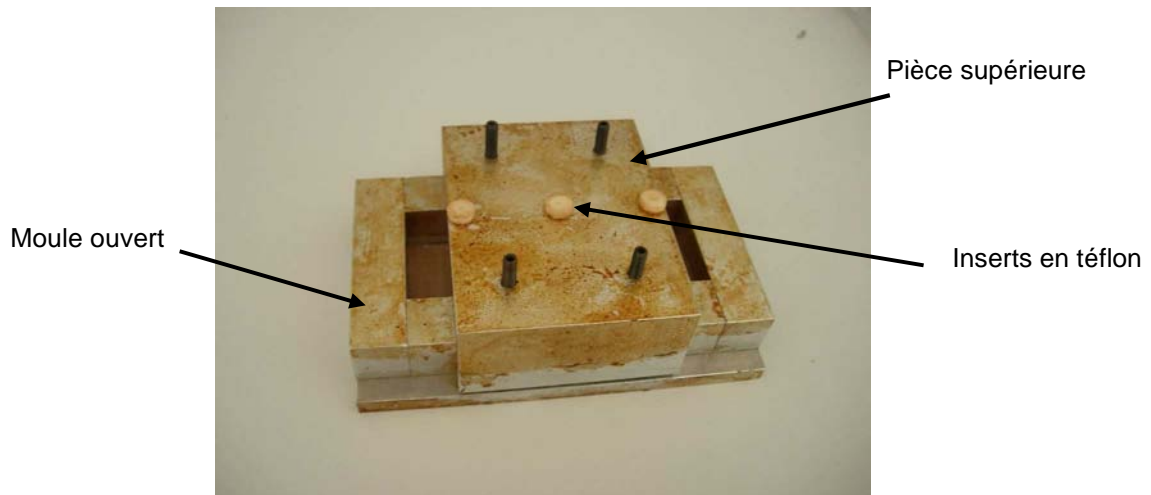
Moule pour la fabrication des éprouvettes de clou noyé dans la résine
